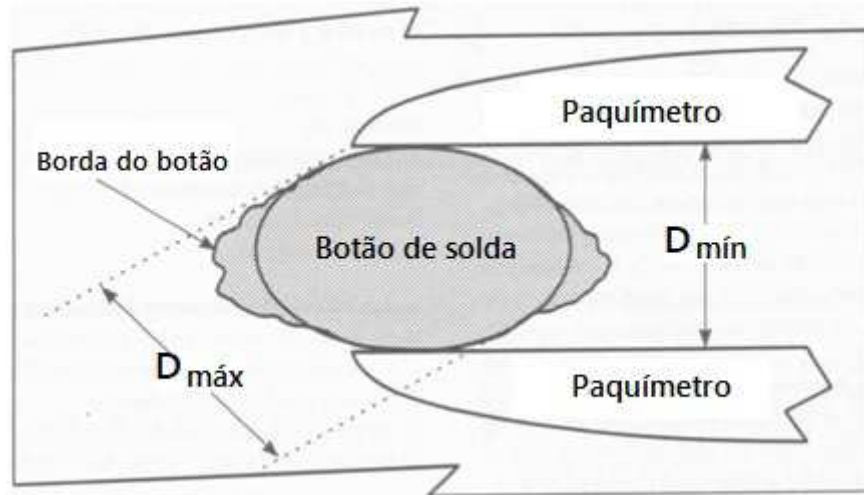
Técnica de medição do diâmetro do ponto de solda.
